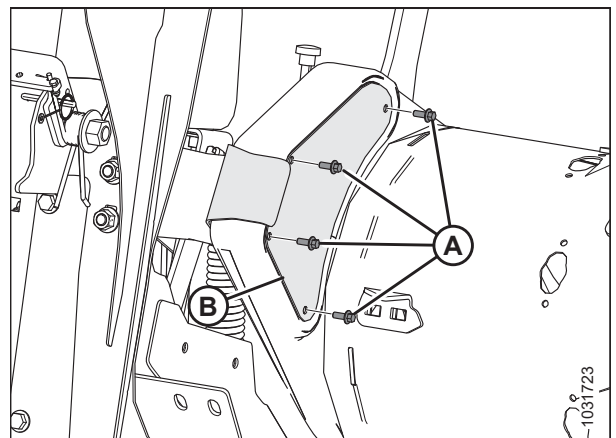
Linke Seite des Einzugsschnecke-Getriebes – Rückansicht
